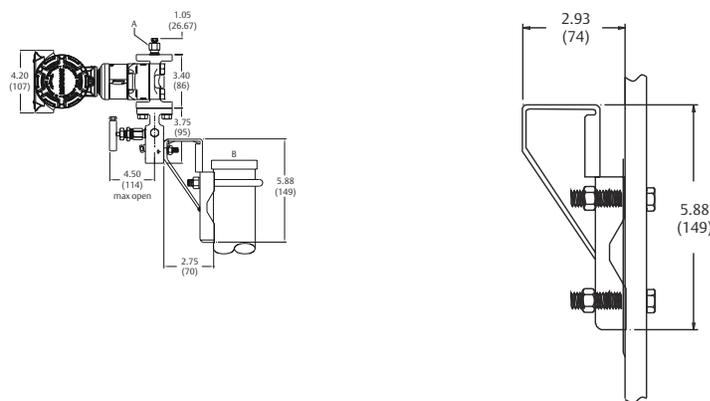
Монтаж кронштейна для копланарного клапанного блока с боковым входом
